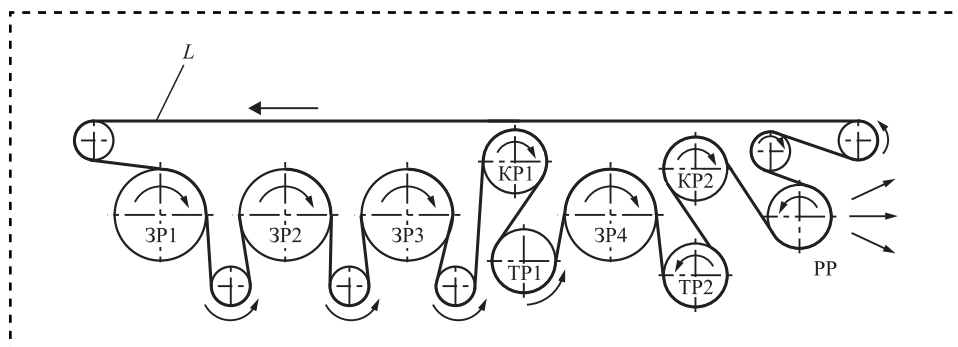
Структура РКЛ СбЦ-15 сборки внутренних катушек втулочно-роликовой цепи: ТР — технологический ротор; ЗР — загрузочный ротор; КР — контрольный ротор; РР — ротор разбраковки
